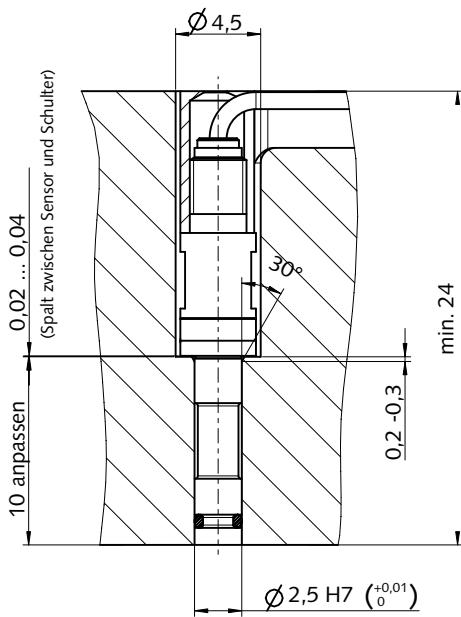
Einbau mit Distanzhülse Typ 6464A1
